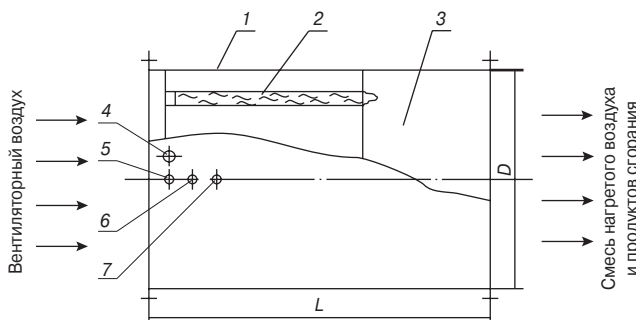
Воздухонагреватель смешительный ВНС: 1 – корпус; 2 – камера горения; 3 – смеситель; 4 – патрубок основной горелки; 5 – патрубок смешительной горелки; 6 – электрод свечи зажигания; 7 – контрольный электрод
